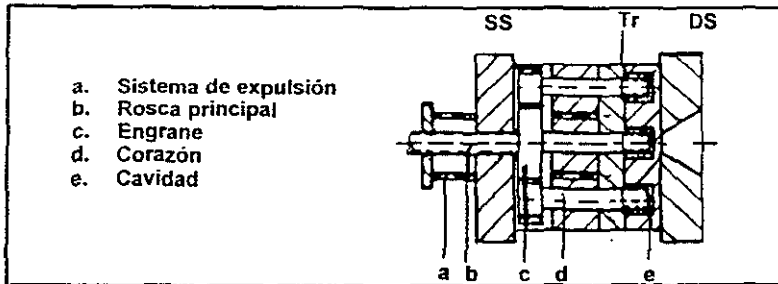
Diagrama Esquemático del Molde con Desenrosque Automático.
